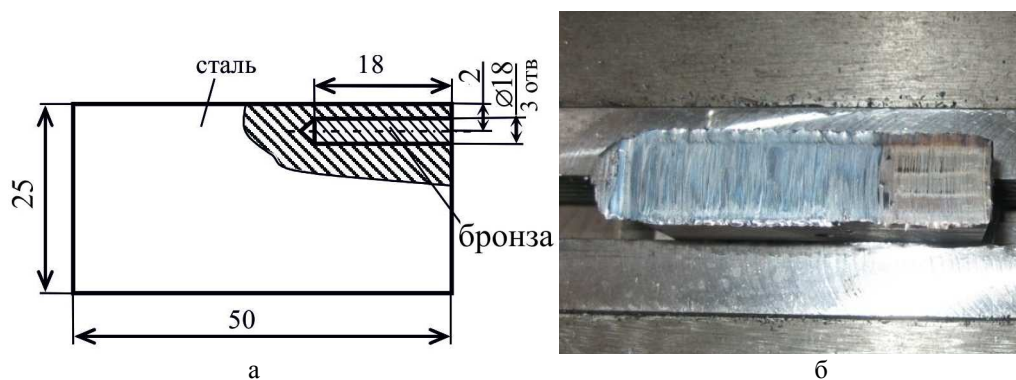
Заготовка из стали 45, в которой помещены стержни из бронзы (а) и общий вид детали после комплексной обработки (б)
